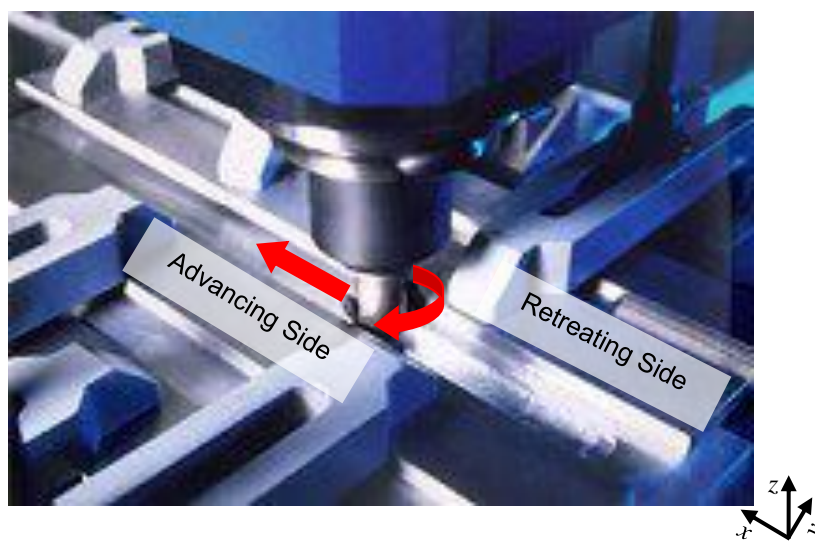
Rotation und Vorschub beim Friction Stir Welding
